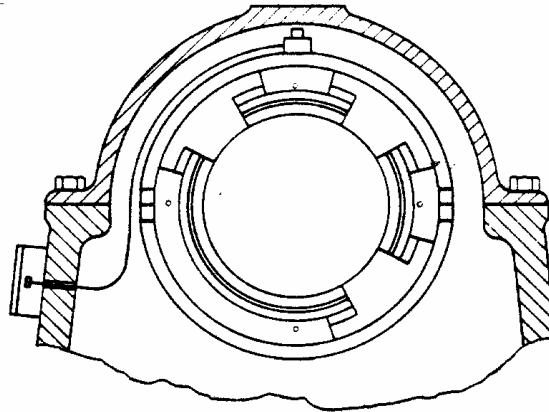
Disposition du capteur dans le cas des machines de grandes dimensions
